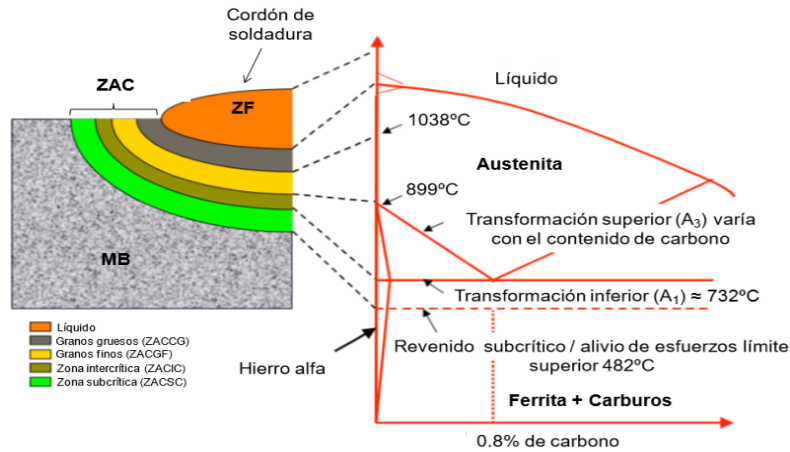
Componentes de una junta de soldadura a tope: metal base, zona afectada por el calor (ZAC), y metal de soldadura. Fuente: Modenesi Marques y (2012).
